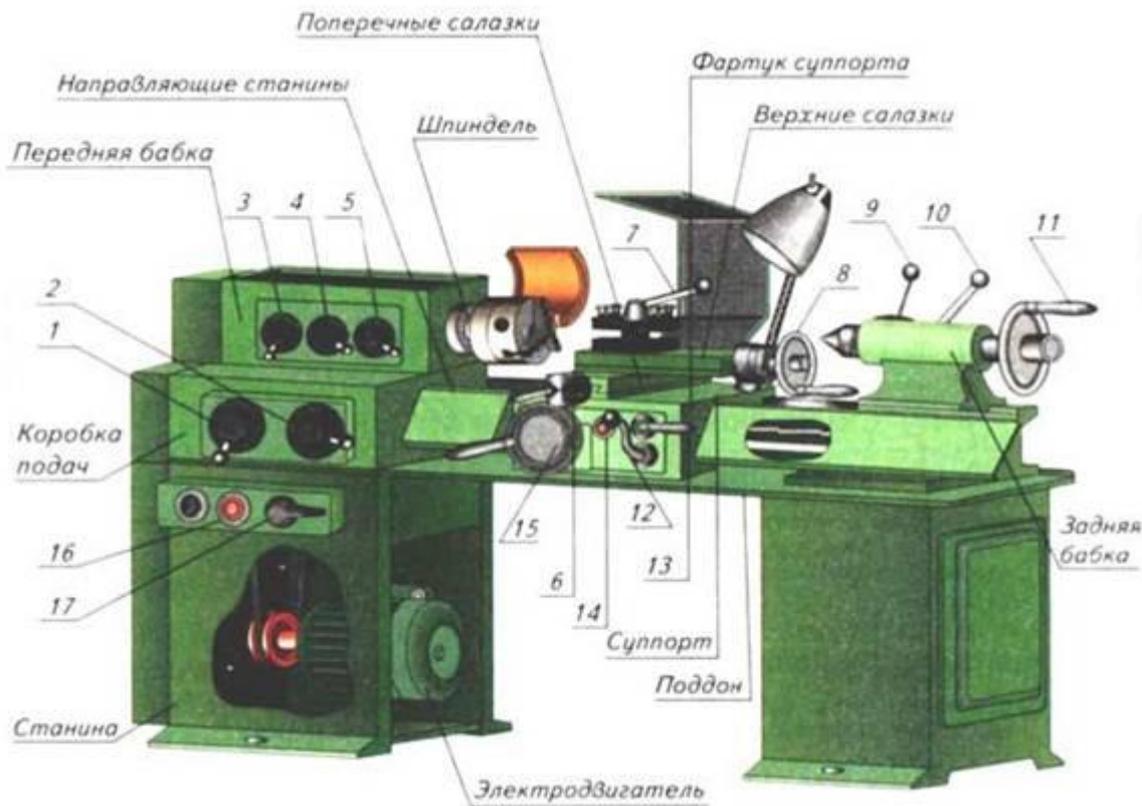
Плакат. Устройство токарно-винторезного станка ТВ-6
